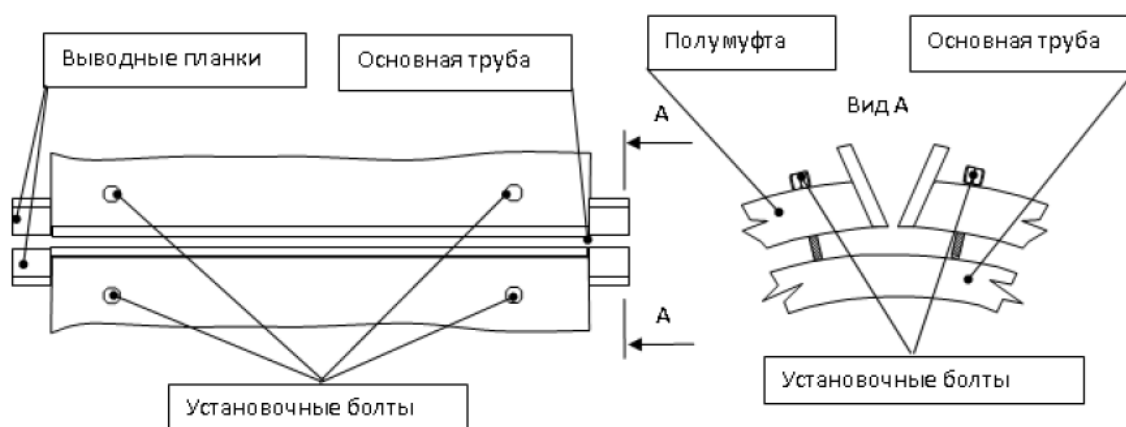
Сборка полумуфта перед сваркой
